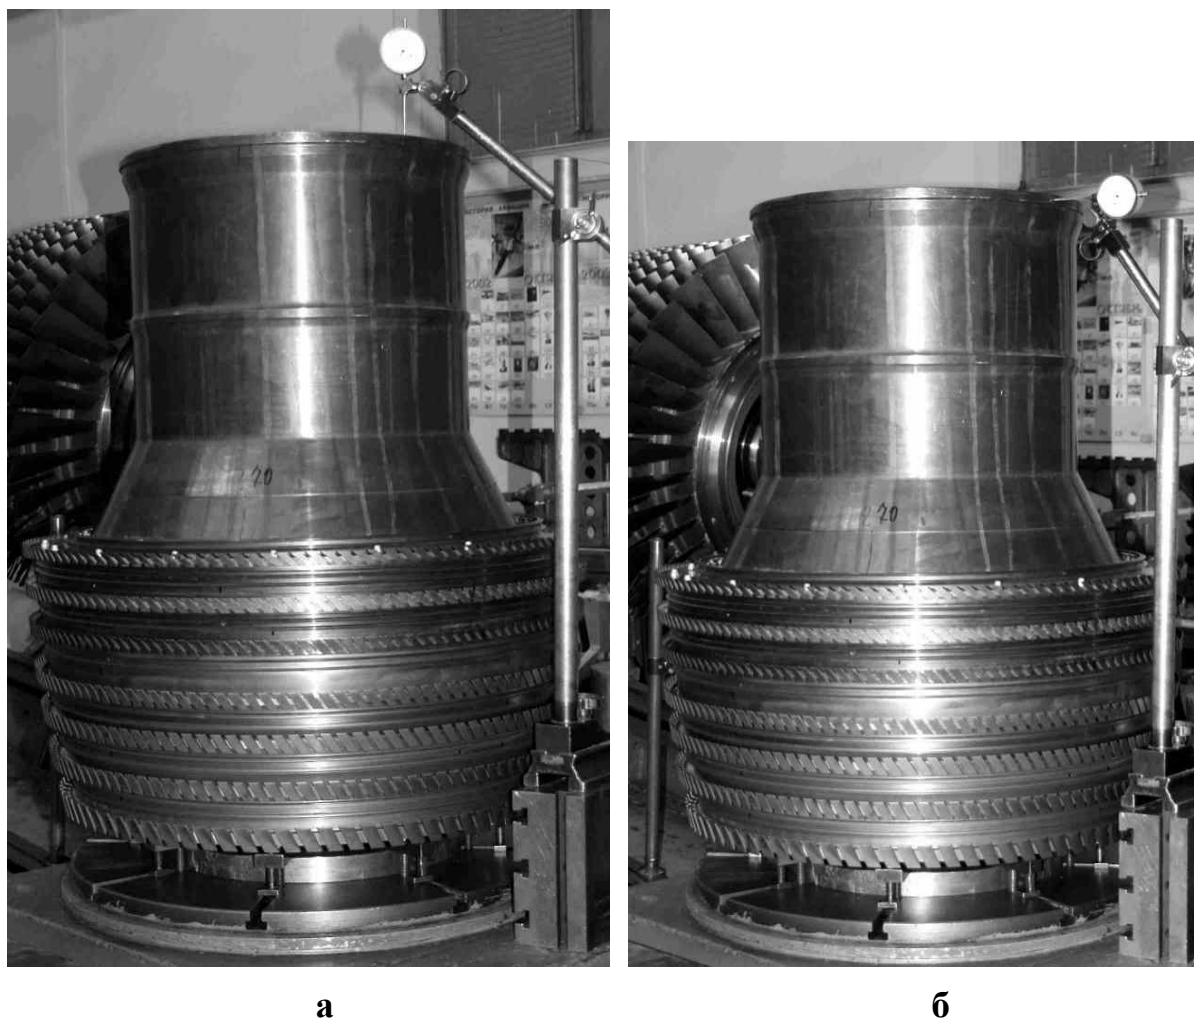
Контроль качества сборки ротора - определение достигнутого положения колеса 7 ст. с валом задним:
